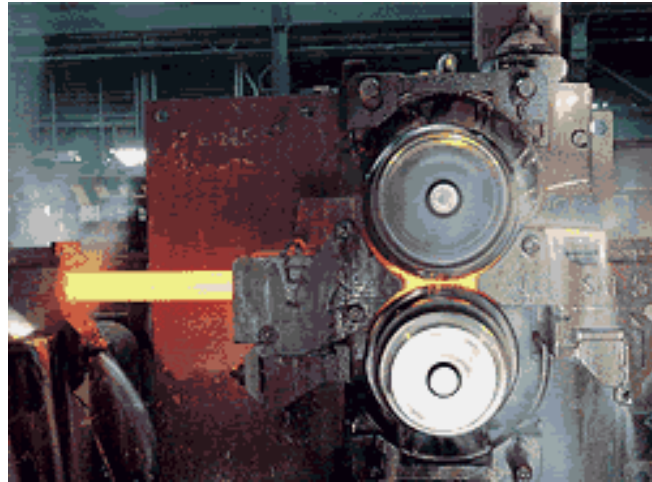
Un molino para laminado plano en caliente, la placa de acero se ve como una tira brillante que se extiende diagonalmente desde la esquina inferior izquierda (cortesía de Bethlehem Steel Company).
